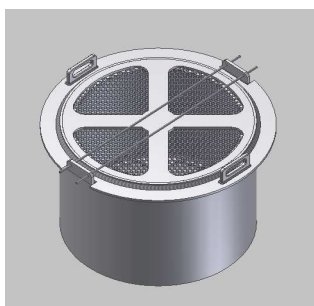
3D-модель корпуса сорбционного фильтра
